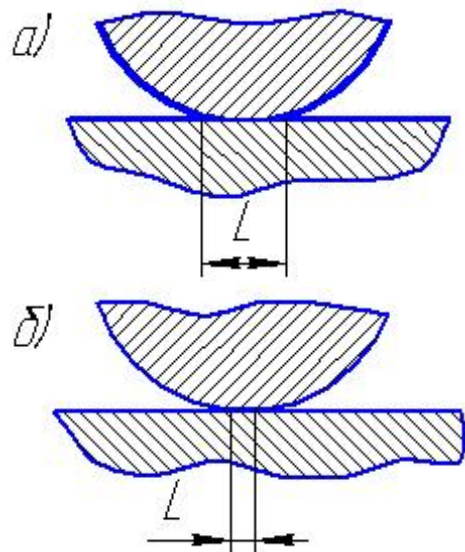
Контакт ролика з кільцем роликового підшипника за наявності металічної плівки (а) і без неї (б)
